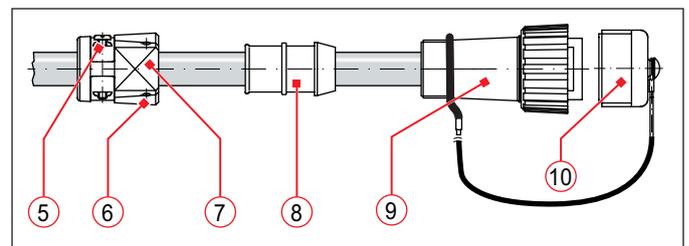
Beispiel für Kabelstecker mit Endgehäuse, Zugentlastung und Verschraubung (gilt analog auch für Kabeldosen)
